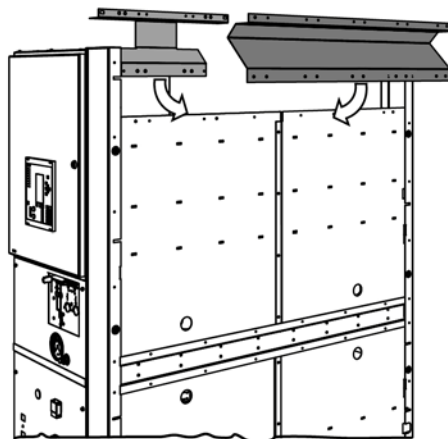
Монтажное положение короткой и длинной металлической пластины для защиты от аварийной электрической дуги
